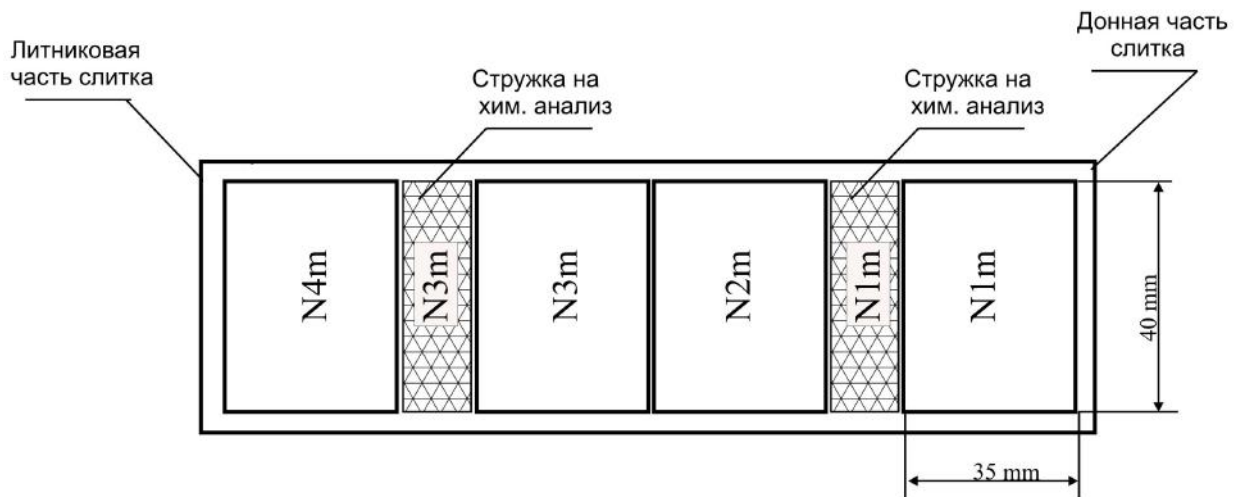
Пример схемы разрезки заготовки СО ЖНС:
